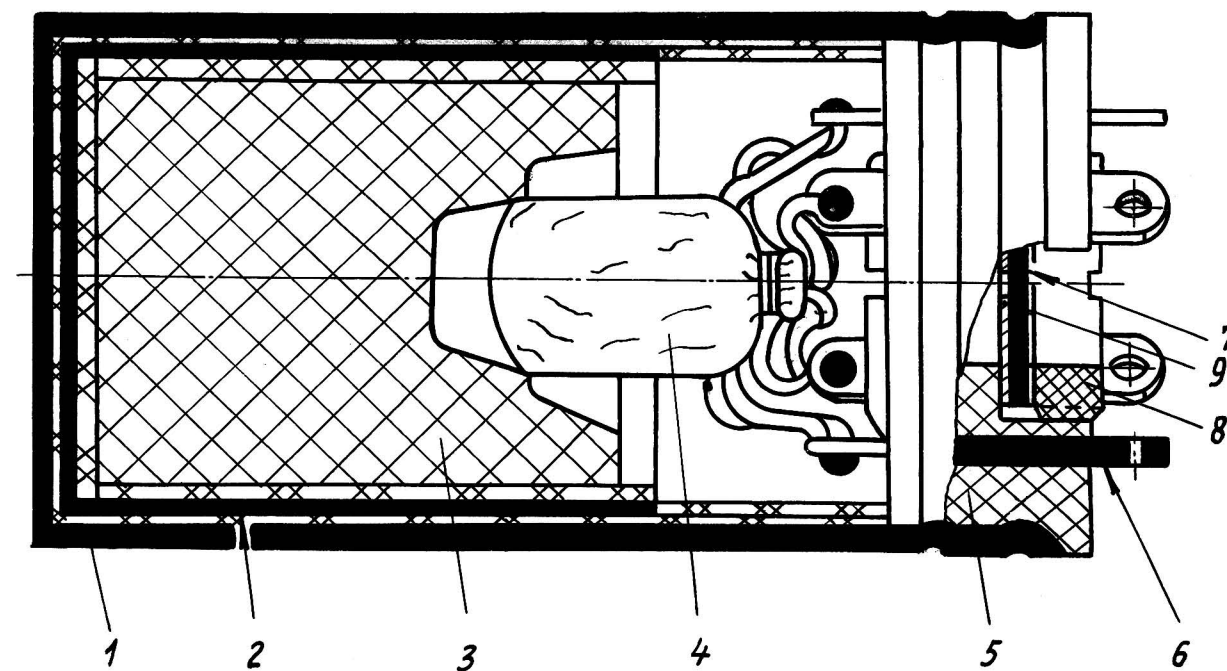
Пирозажигательный патрон ППЗ-6А;
